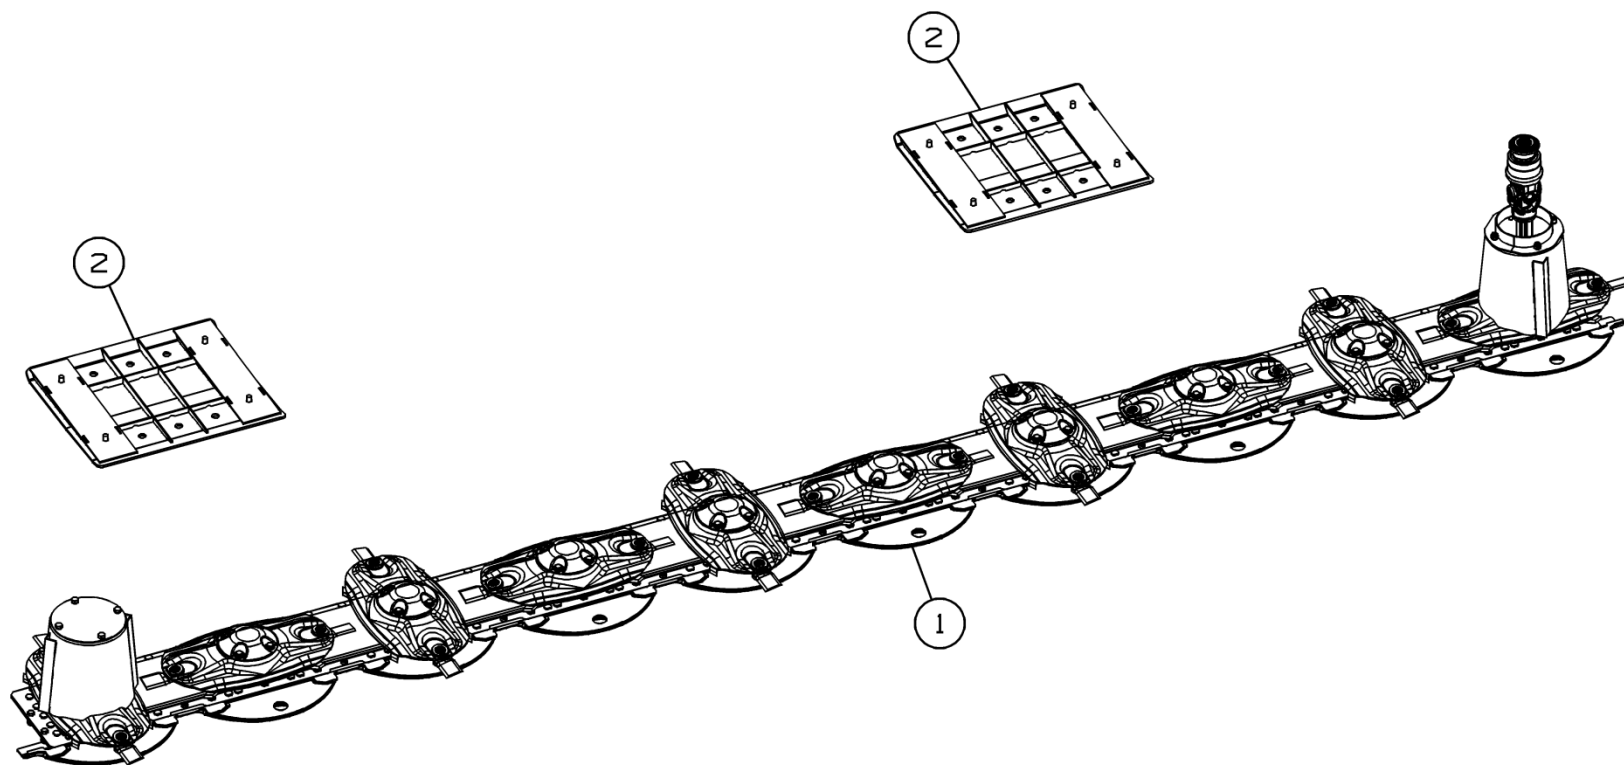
Установка брусьев режущих и башмаков опорных GM-500R.01.04.000A
